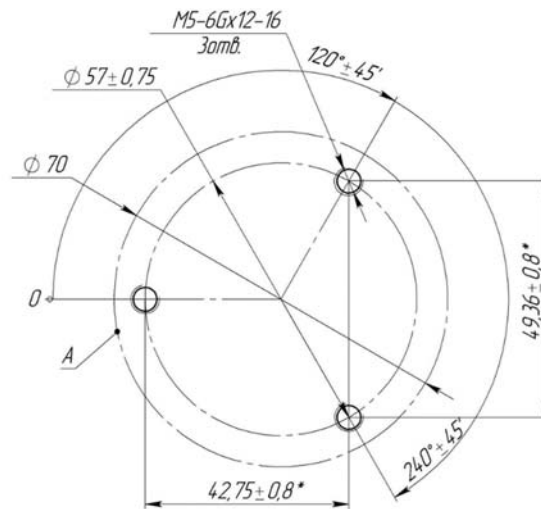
в. Установочные размеры и требования к поверхности вибропреобразователя ВК-310
